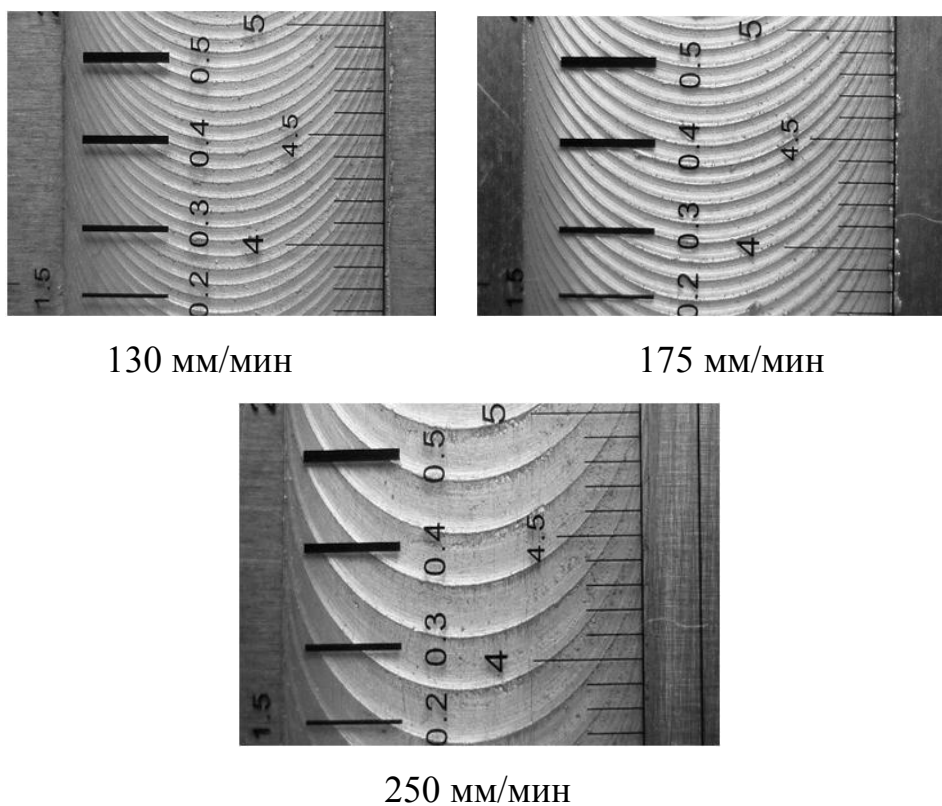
Кольцевой рельеф поверхности сварного шва сплава системы Al–Cu–Mg при разных скоростях подачи рабочего инструмента (скоростях сварки)
